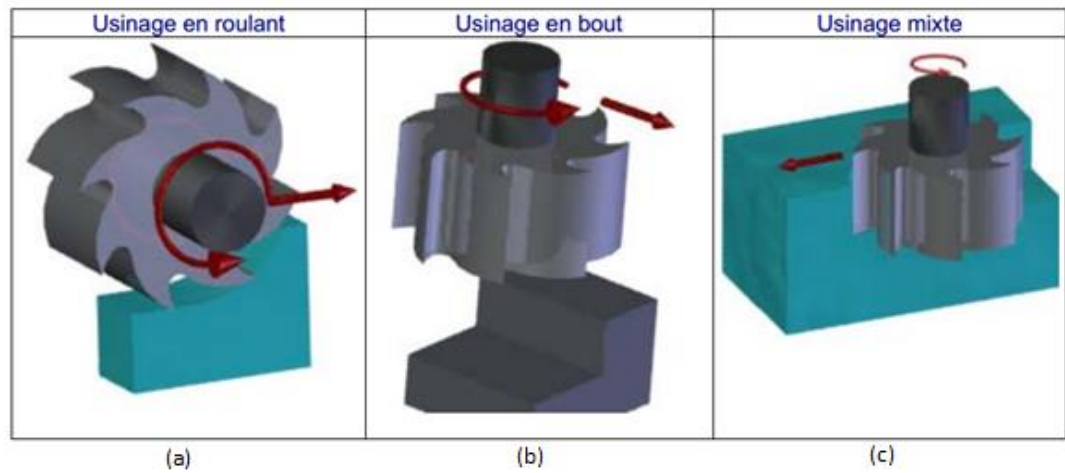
Les différents types d'usinage en fraisage : (a) en roulant, (b) en bout et (c) mixte [10].
